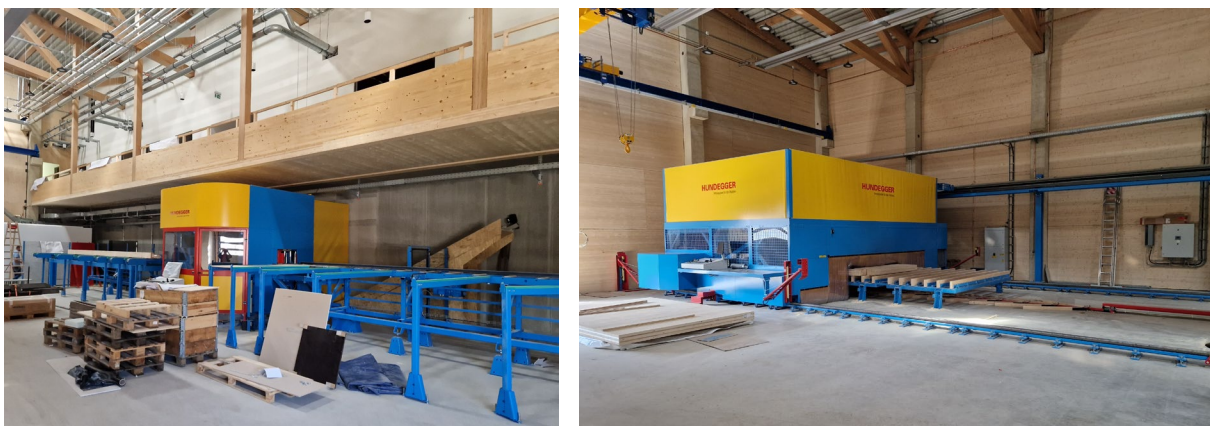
Abbundmaschinen für stabförmige Bauteile bis 9 m (links) und plattenförmige Bauteile (rechts)
